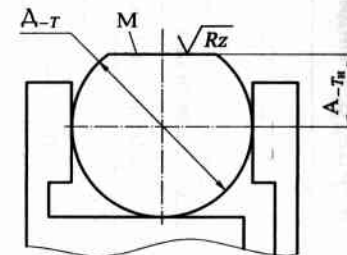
Схема базирования цилиндрической заготовки при обработке плоской поверхности
